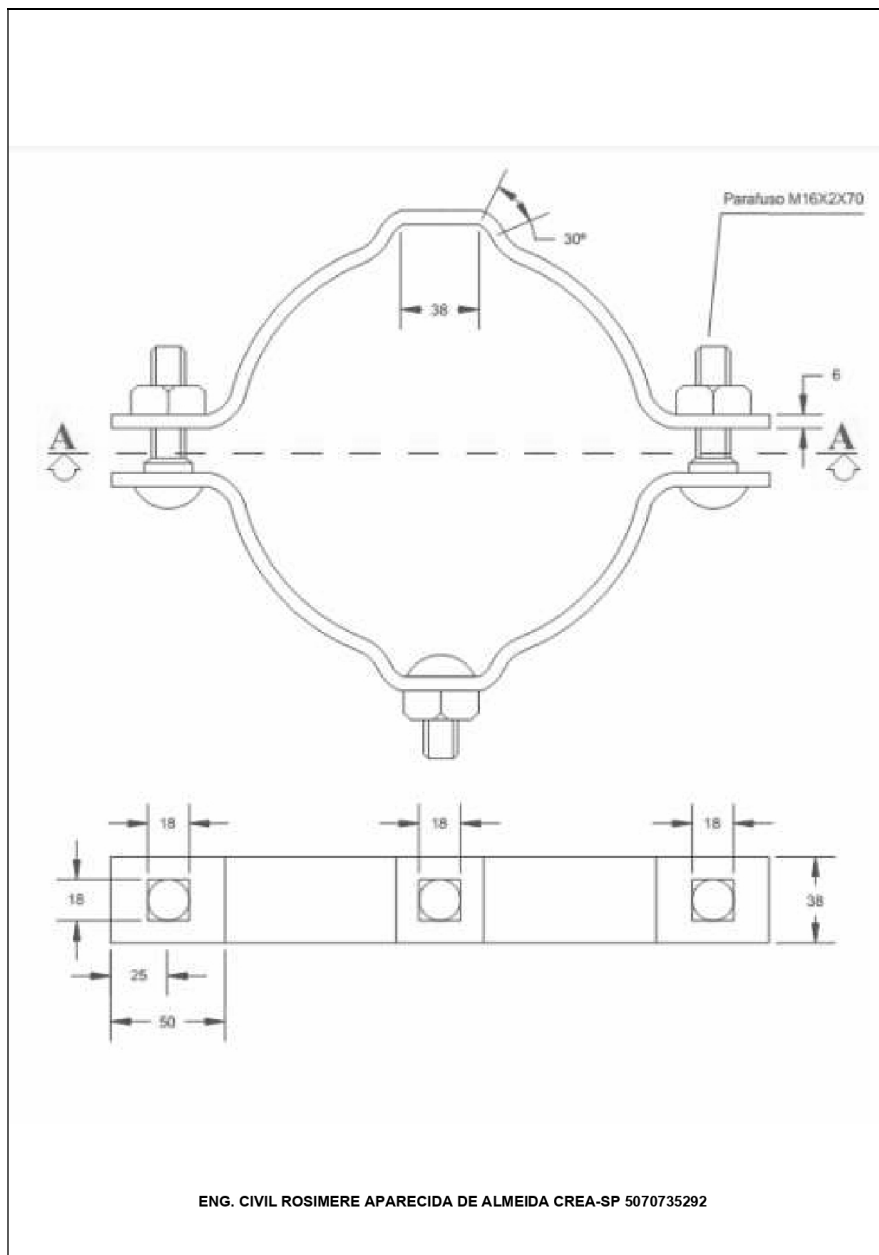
ABRAÇADEIRA METÁLICA PADRÃO
